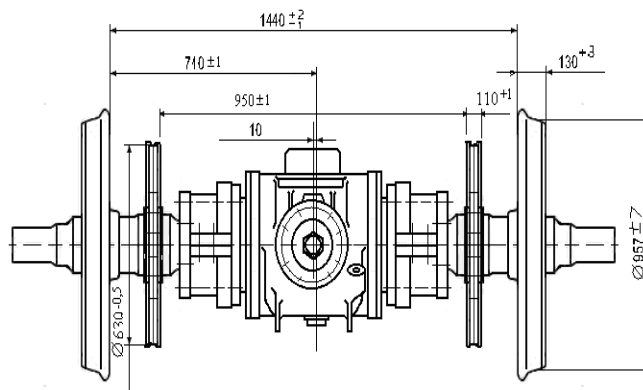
Колесная пара 4096.15.010СБ с тормозными дисками «Knorr-Bremse» и редуктором
